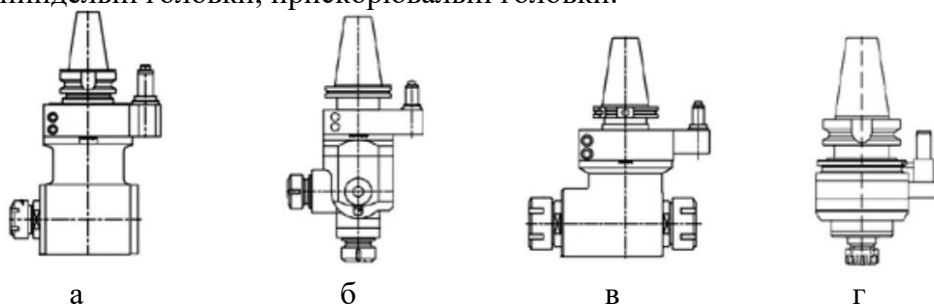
Приводний інструмент для верстатів фрезерної групи з числовим програмним керуванням: державний цанговий держак (а); поворотний цанговий держак (б); радіальний цанговий мультиплікаторний держак (в); прискорювальна головка (г)
